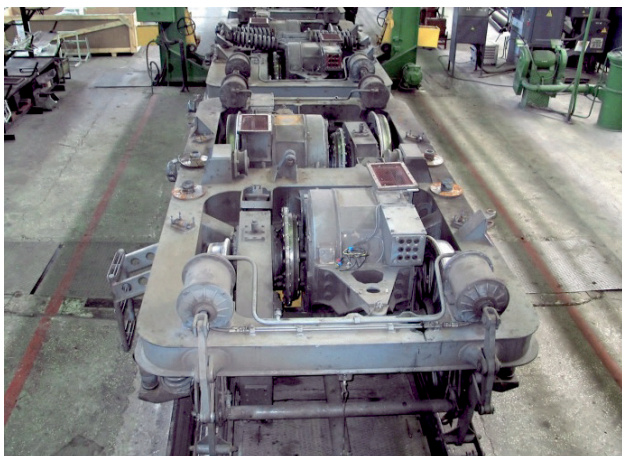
Внешний вид тягового двигателя в составе тележки электровоза
